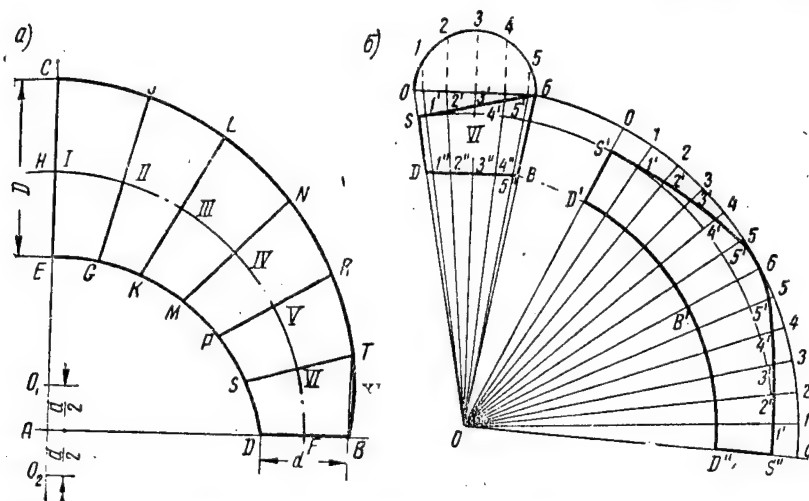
Разметка конусного колена: а — боковой вид; б — построение развертки сектора.
